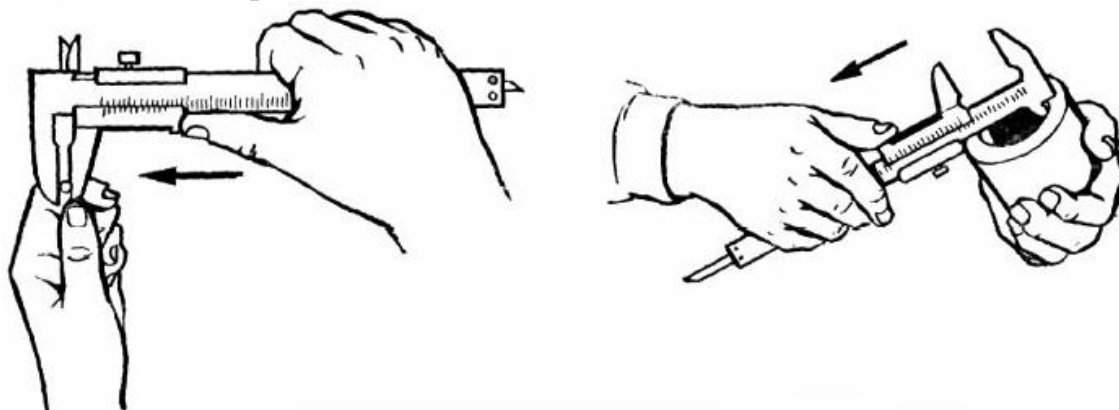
Вимірювання штангенциркулем зовнішніх (а) та внутрішніх (б) розмірів не закріпленої деталі
